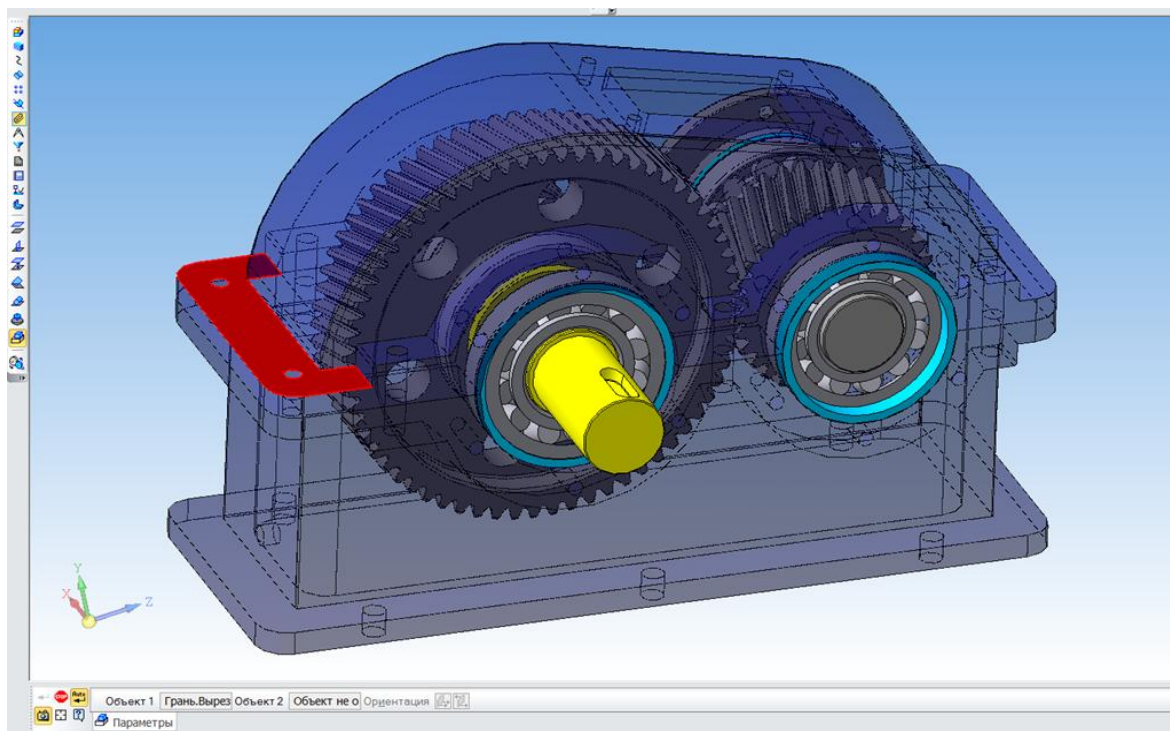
Снимок экрана при установке готовой под сборки в корпус редуктора
